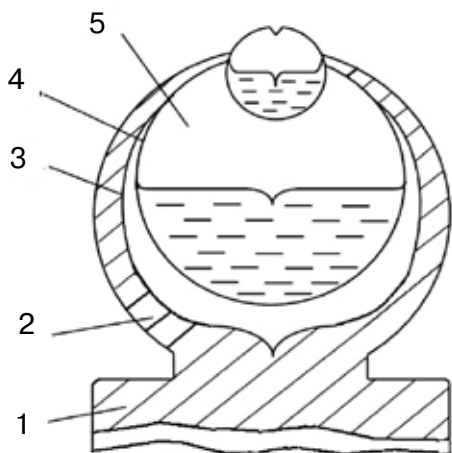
Схема питания отливки шаровой прибылью при ЛГМ: 1 – отливка; 2 – прибыль; 3 – корка металла; 4 – окружность; 5 – газовая фаза
